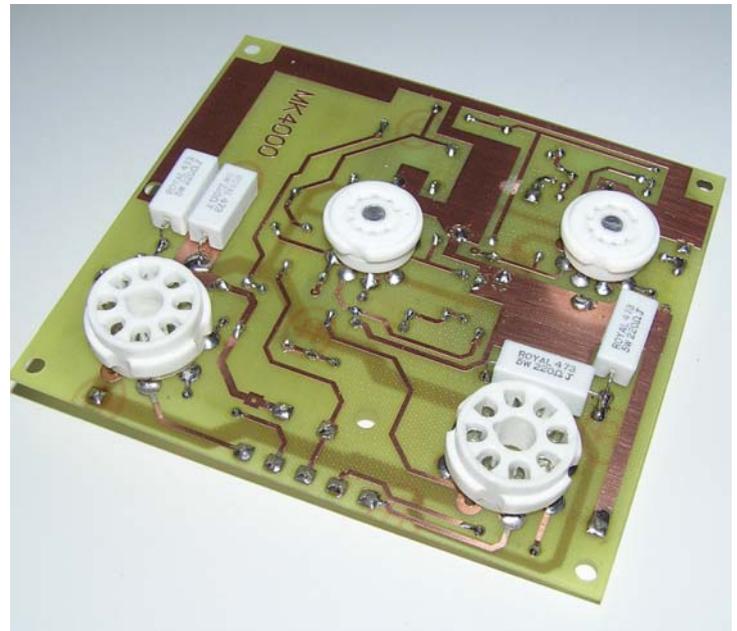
Plano de montaje lado componentes de la tarjeta MK4000
